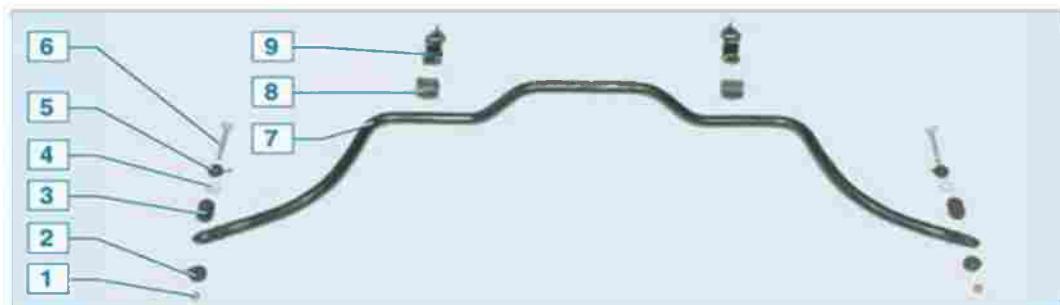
Элементы стабилизатора поперечной устойчивости: 1 - гайка; 2 - нижняя резиновая втулка; 3 - промежуточная резинометаллическая втулка; 4 - пластмассовая шайба; 5 - верхняя резиновая втулка; 6 - винт; 7 - штанга стабилизатора; 8 - скоба; 9 - подушка штанги стабилизатора.
